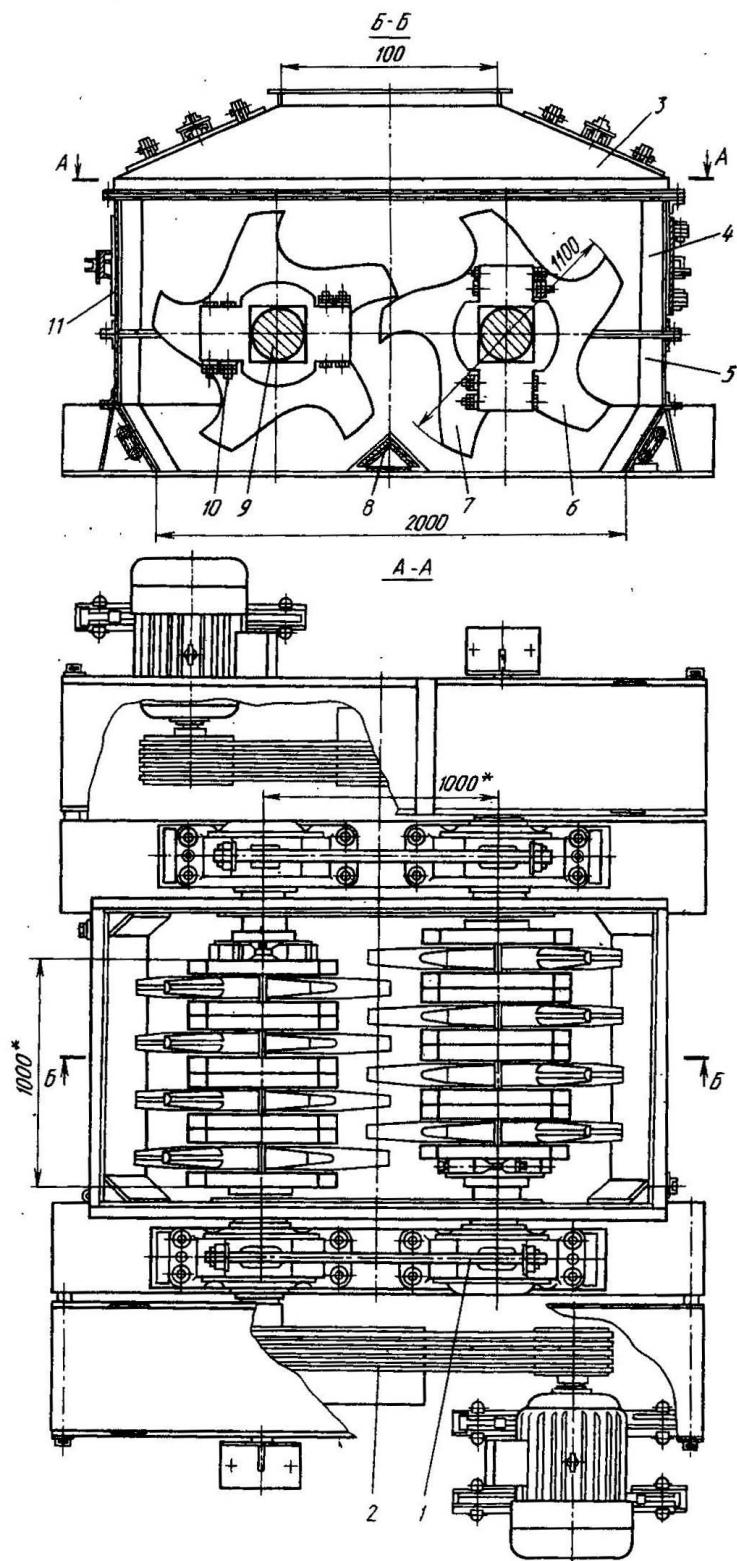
Двухвалковая зубчатая дробилка СМД-153
